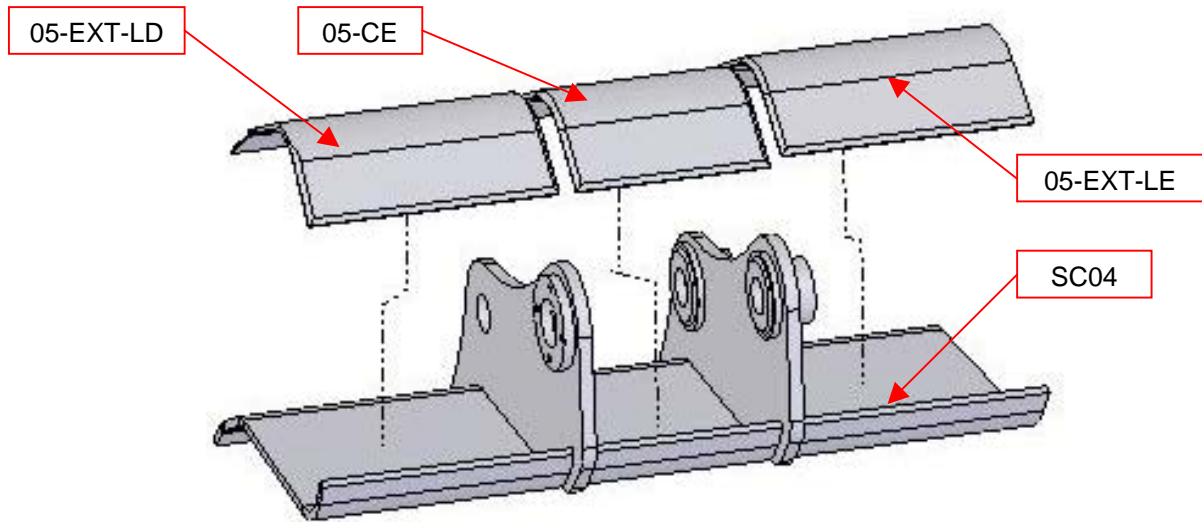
Vista explodida do subconjunto 05 - SC05.
